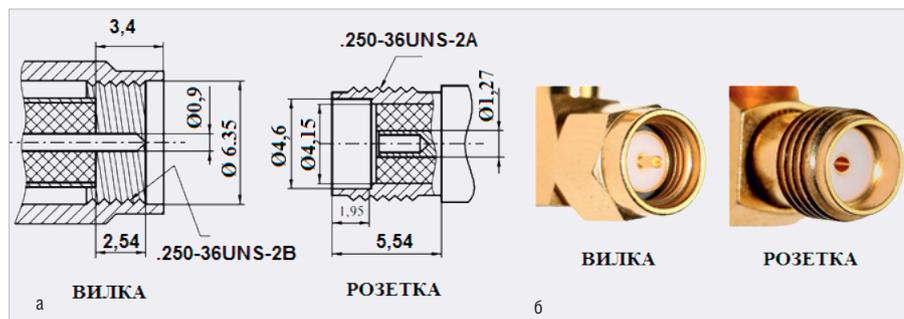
Вилки и розетки соединителей SMA: а) интерфейс; б) внешний вид
